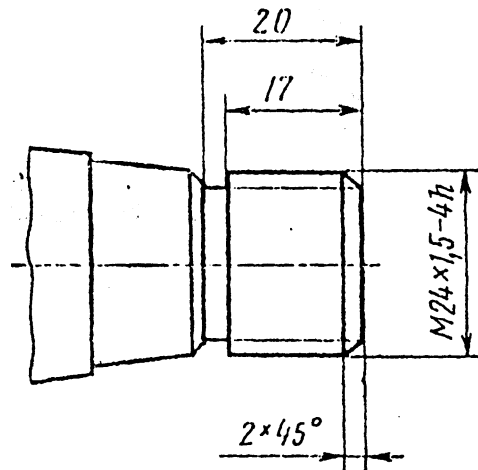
Ескіз обробки різьби поворотного кулака після наплавлення
